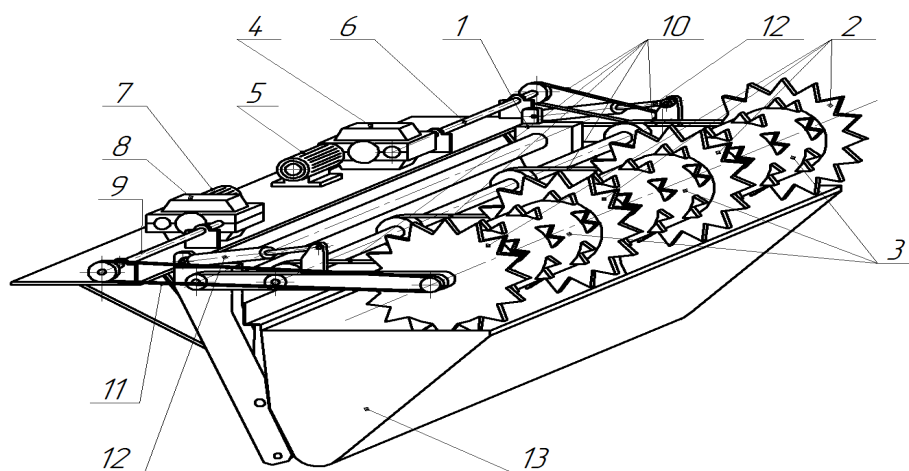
Схема экспериментальной установки: 1 – рама; 2 – фрезы; 3 – отделяющие барабаны; 4, 8 – редуктор, 5, 7 – электродвигатель; 6 – тензометрический вал фрез; 9 – тензометрический вал отделяющих барабанов; 10, 11 – ременные передачи; 12 – гидроцилиндры; 13 – ковш
